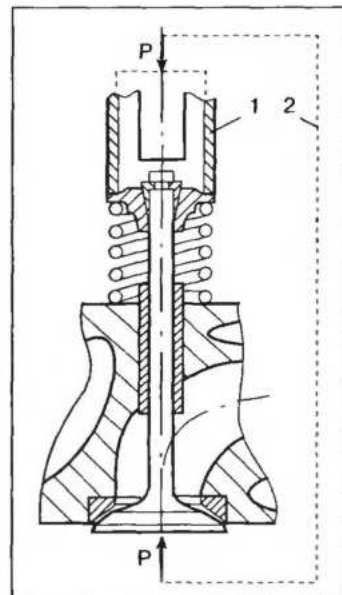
Общая схема работы приспособлений для разборки/сборки пружин клапанов: 1 — нажимающее кольцо приспособления; 2 — силовая связь, обеспечивающая усилия P нажатия на тарелку пружины и упора в тарелку клапана
